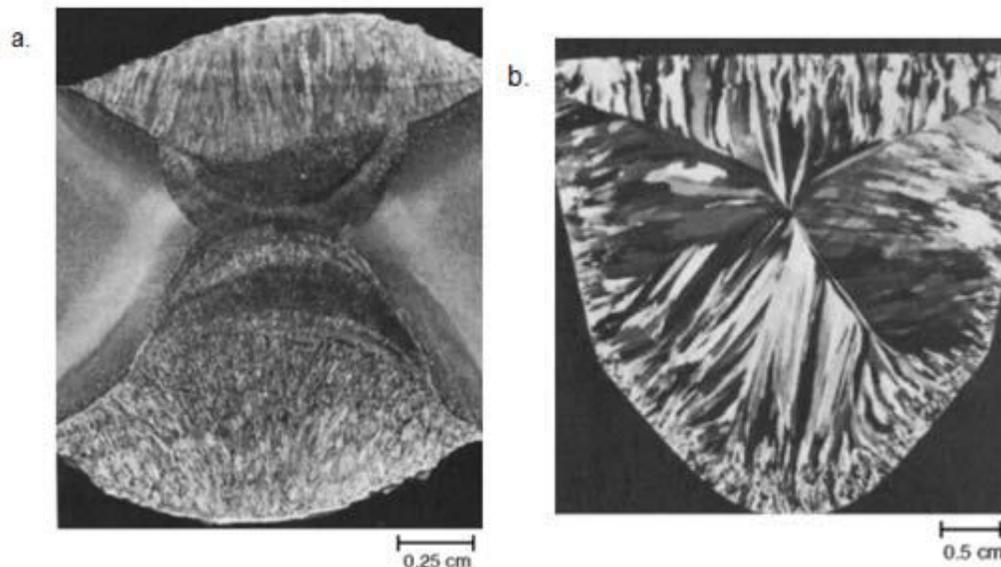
(a) Sección a través de una arco de soldadura a tope. (b) Macroestructura, muestra de un lingote de aluminio aleado (1).
